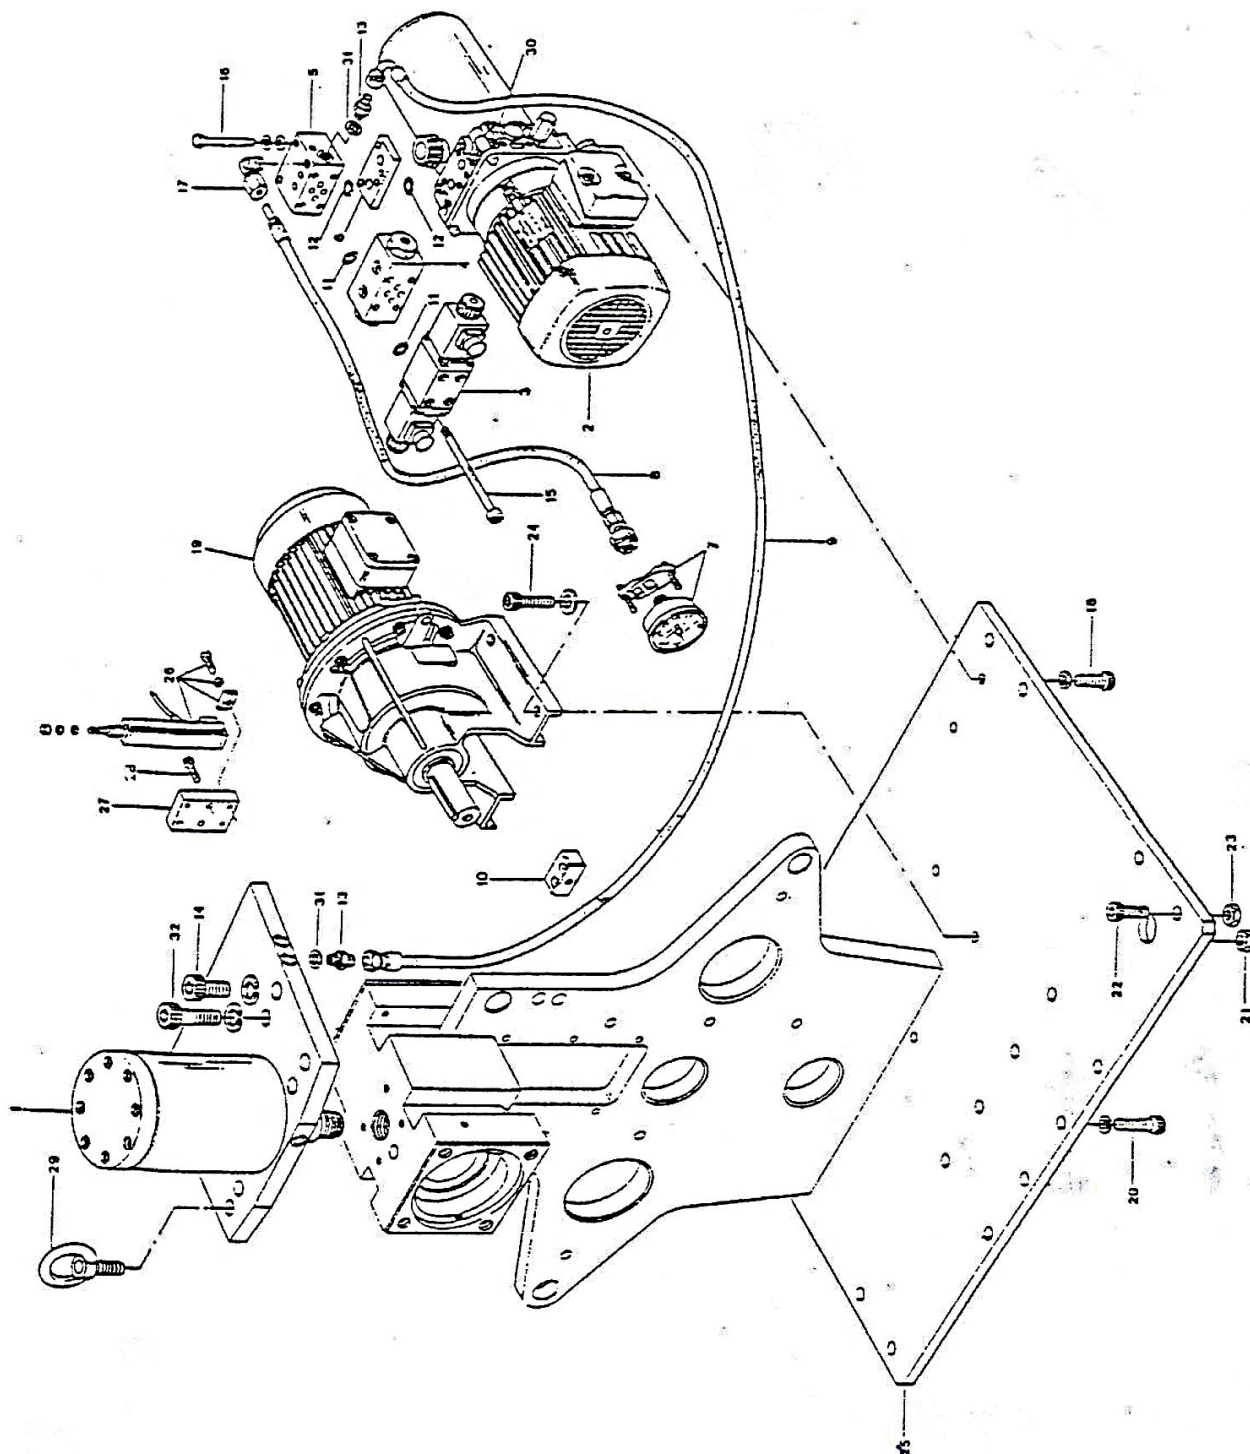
Dessin des pièces détachées 2 PRM 60 FH
